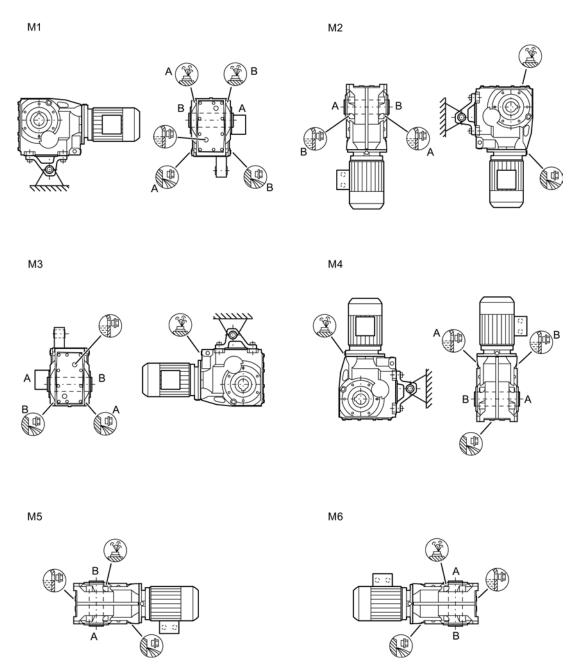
Posiciones de montaje para reductor de ejes perpendiculares KAD en versión enchufable, tamaños 39 - 149
